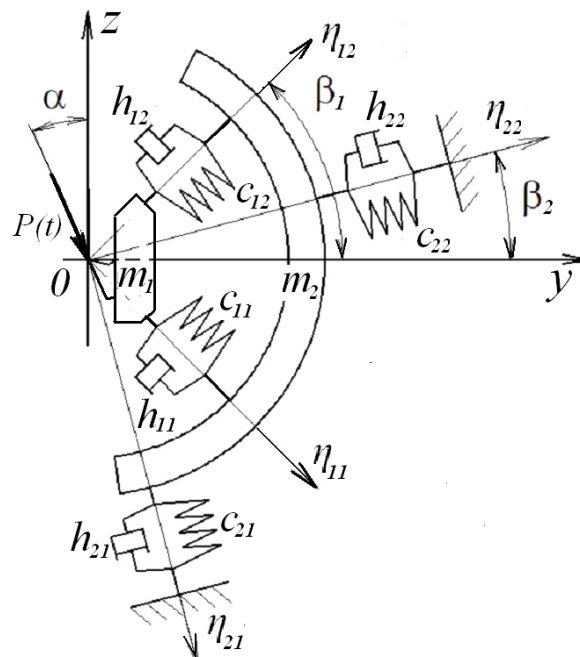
Розрахункова схема пружної системи різець-супорт токарного верстата
